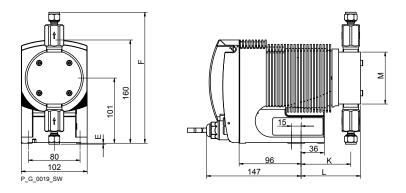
Габаритный чертеж gamma/L, материал SST - размеры в мм
